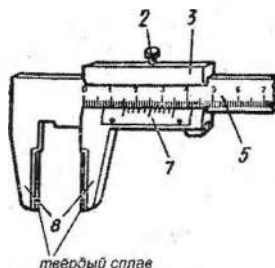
Штангенциркуль ШЦТ-I (с губками, оснащёнными твёрдым сплавом): 2 — зажим, 3 — рамка, 5 — штанга, 7 — нониус, 8 — губки для наружных измерений [10, с. 153]
